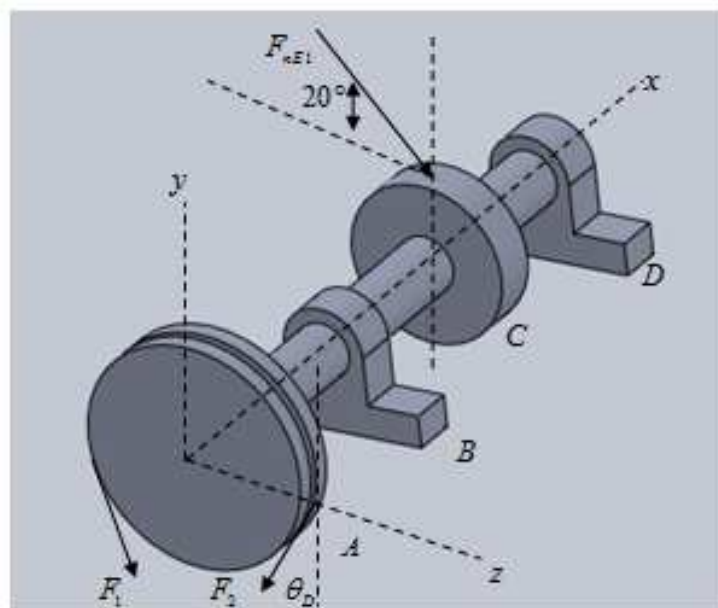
Disposición de la polea mayor y el engrane 1 sobre el eje 1
